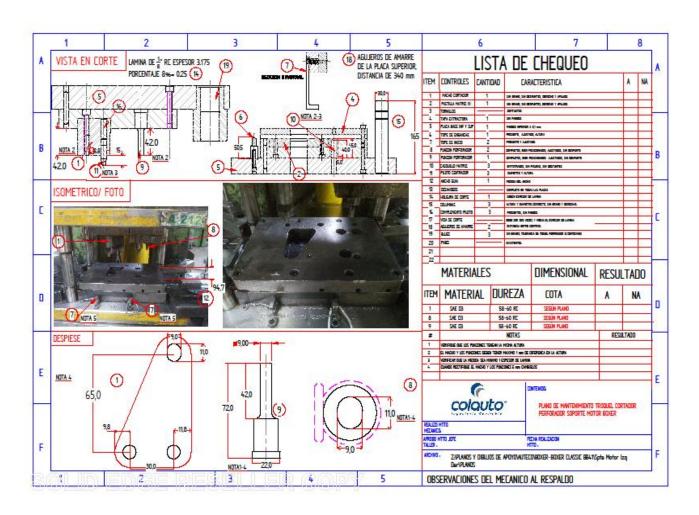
Diseño del troquel para montaje de sensores, Fuente: (Colombia Patente nº BB 410, 2018)
